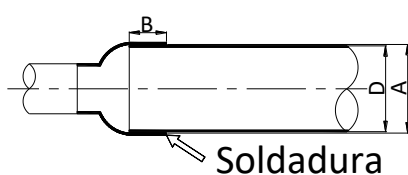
Orientación de tuberías durante la soldadura
